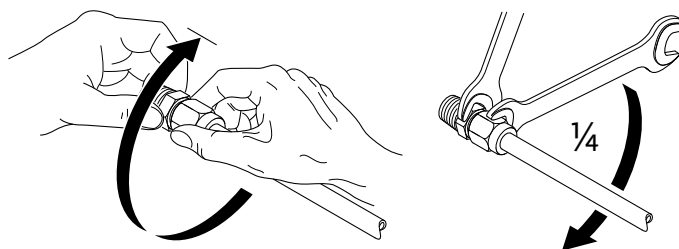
Дополнительный поворот резьбового соединения с обжимным кольцом на 1/4 оборота
